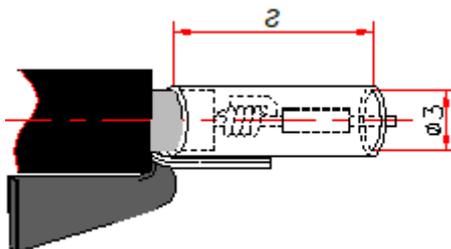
Изоляция корпуса резистора термоусадочной трубкой
